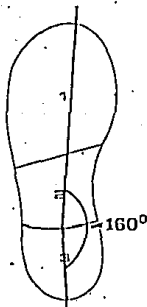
En el calzado normal, entre el eje de la planta (comprendido el enfranque) y el eje del talón existe un ángulo de aproximadamente 160°.
